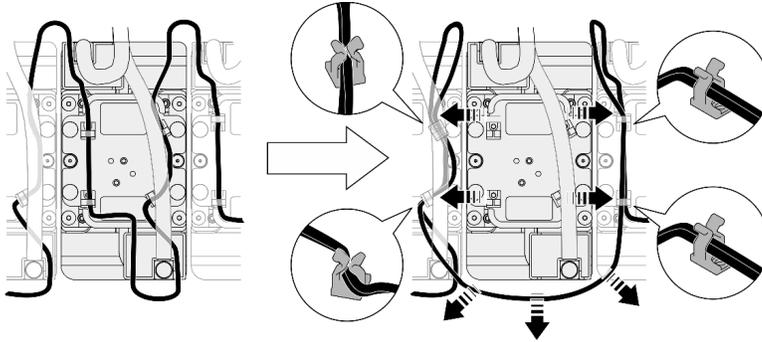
Removendo os cabos do módulo do sensor de vazamento
